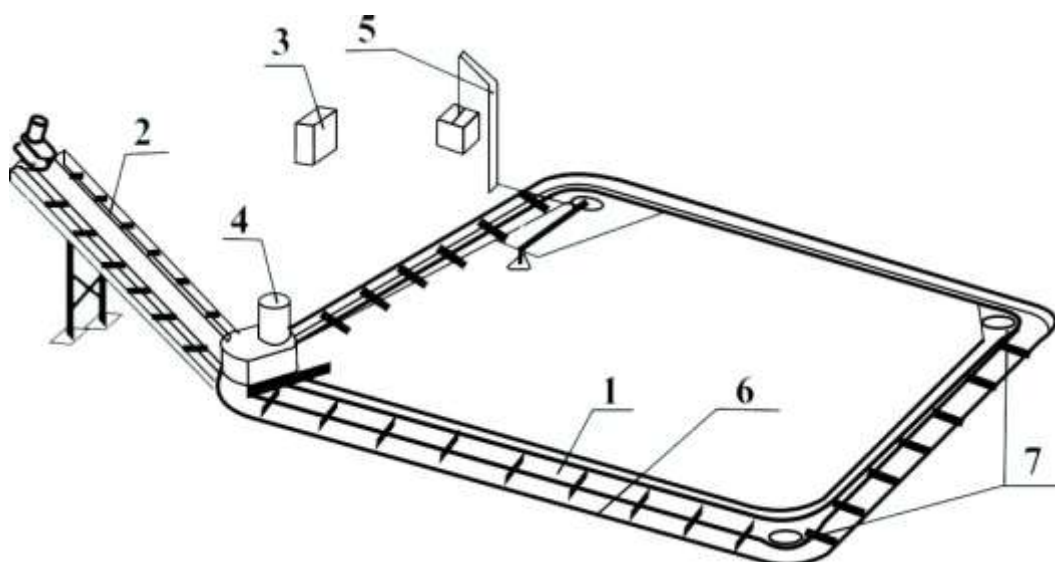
Транспортёр скребковый навозоуборочный ТСН-160:
